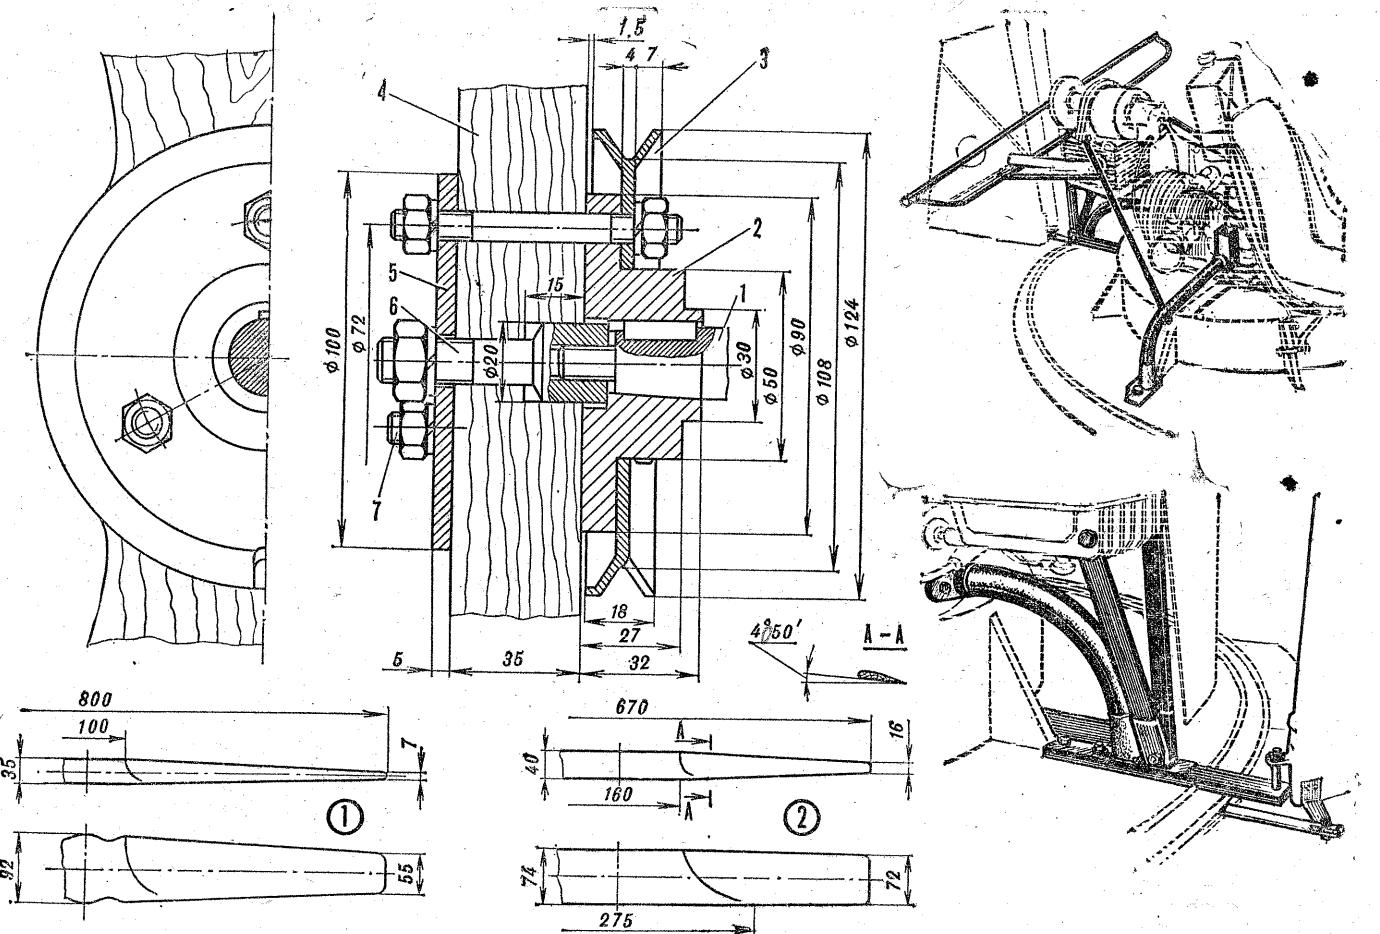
Заготовки воздушных винтов: 1 — маршевого и 2 — нагнетателя.
